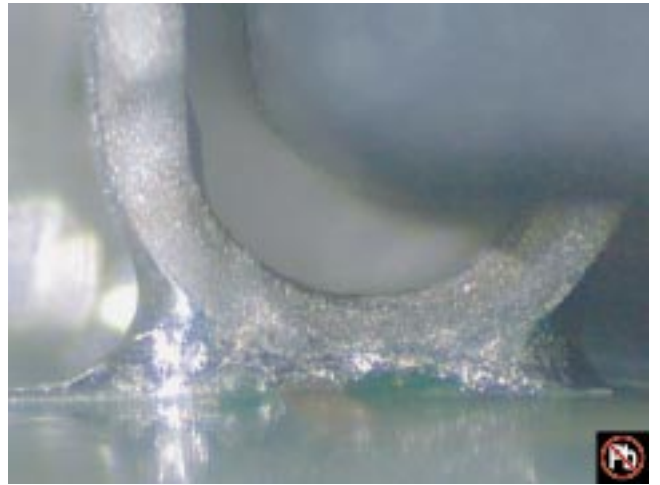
Soldadura SnAgCu; Proceso No-Lavable; Reflujo de Aire
